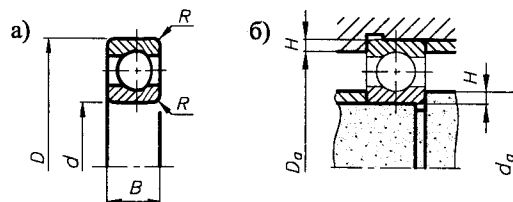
Размеры подшипников для их установки: а) габаритные размеры; б) установочные размеры (размеры заплеchkов)
